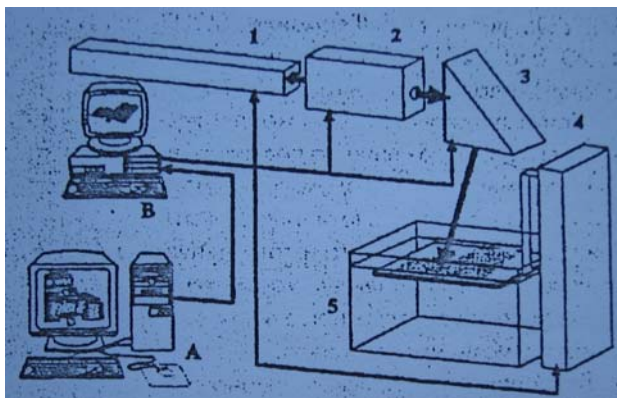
Схема установки для изготовления моделей с использованием лазерной стереолитографии. 1 – HeCd-лазер; 2 – акустико-оптический затвор; 3 – двухкоординатный сканатор; 4 – элеватор; 5 – емкость с жидким фотополимером.
